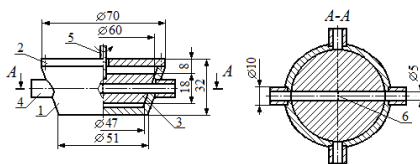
Схема дозатора ионита (повернуто): 1 – корпус; 2 – крышка; 3 – пробка; 4 – штуцер; 5 – вал; 6 – сетка
